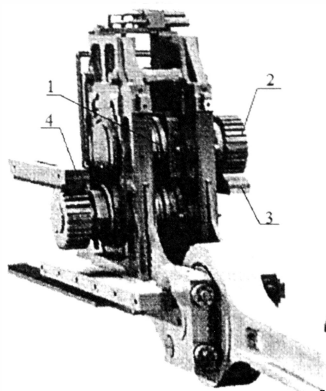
Привод клетки стана ХПТ. 1- валок с переменным ручьем калибра, 2 – ведущая шестерня, 3 – нижняя рейка, 4- верхняя рейка
